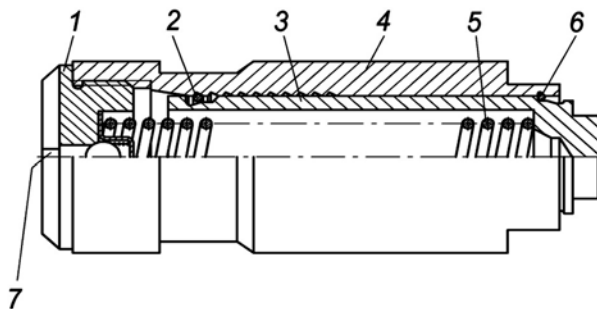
Гидронатяжитель 406.1006100-20: 1 – клапан в сборе; 2 - запорное кольцо; 3 - плунжер; 4 - корпус; 5 - пружина; 6 - стопорное кольцо; 7 - отверстие подачи масла
